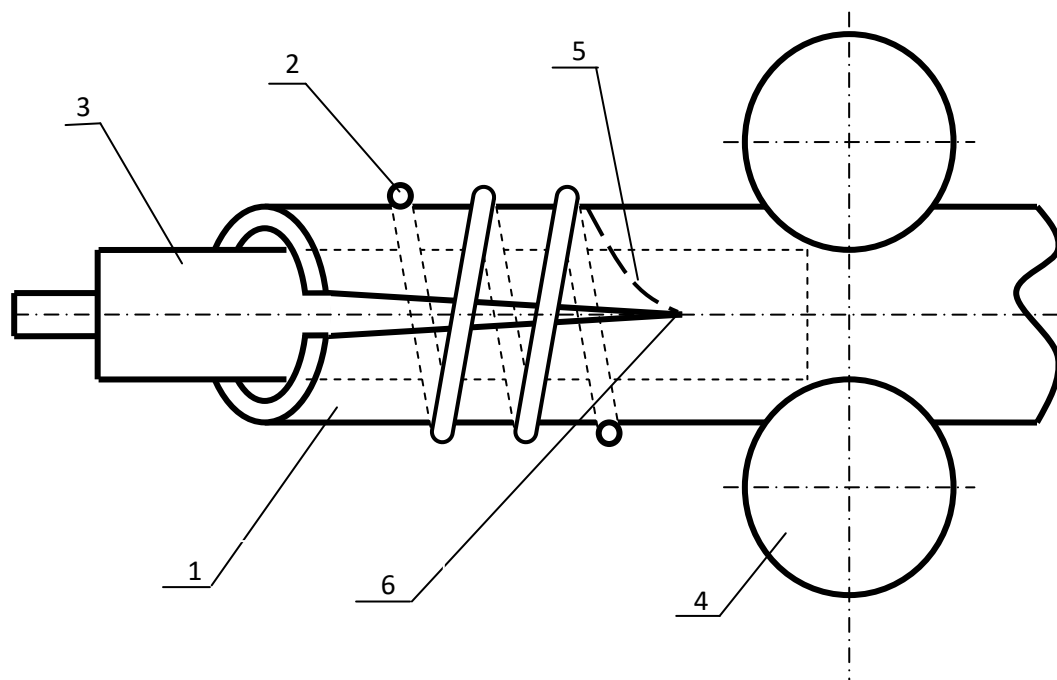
Схема высокочастотной сварки с индукционным подводом тока к кромкам трубной заготовки: 1 – трубная заготовка, 2 – кольцевой двухвитковый индуктор; 3 – ферритный стержень; 4 – валки сварочной клетки; 5 – путь тока; 6 – точка схождения кромок.
